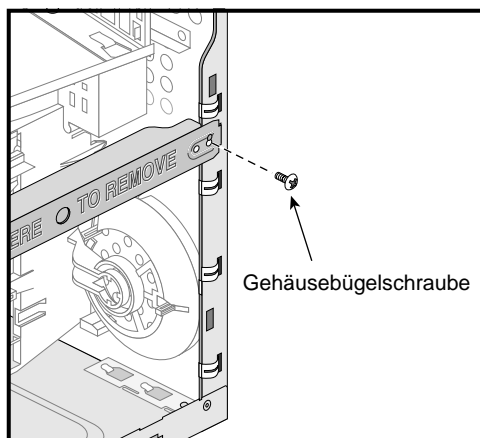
Anbringen der Schraube am Gehäusebügel
